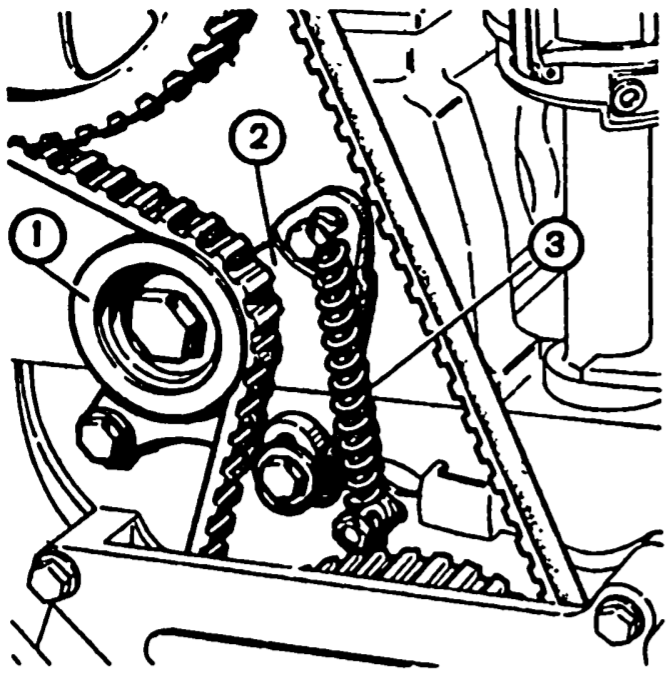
Механизм натяжения ремня привода распределительного вала: 1 - натяжной ролик; 2 - кронштейн натяжного ролика; 3 - натяжная пружина
